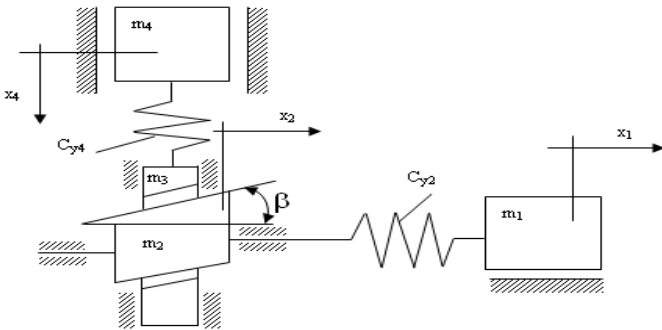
Клиновой механизм:  $m_i$  - масса;  $P_i$  - вес;  $C_{y2}$  - жесткости зубчатого редуктора, штока с опорным устройством привода;  $x_i$  - координата;  $\beta$  - угол подъема резьбы винта;  $i = \overline{1,4}$  (1 – электродвигатель; 2 – ходовая гайка; 3 – ходовой винт; 4 – неуравновешенная нагрузка).
